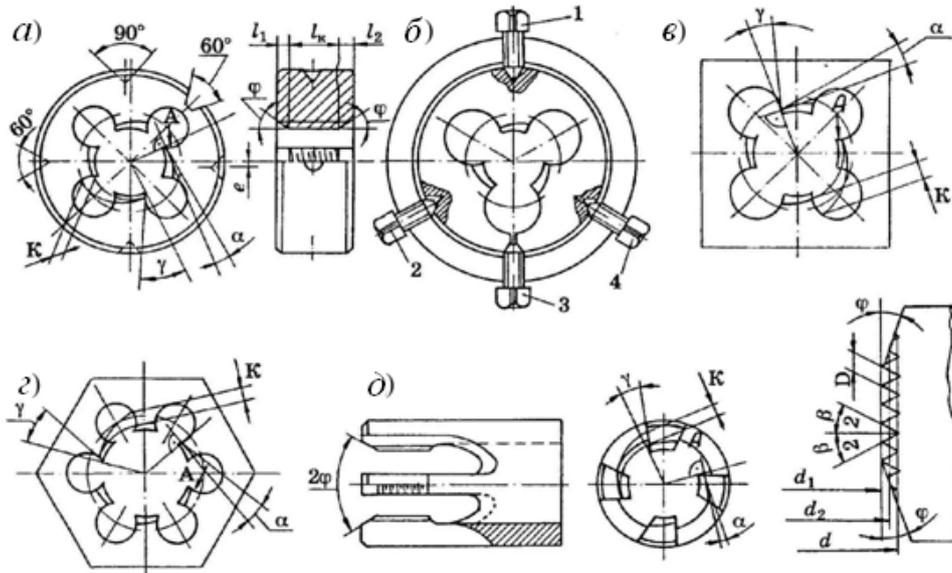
Резьбонарезные плашки (а, в – д) и их крепление в плашкодержателе (б)
